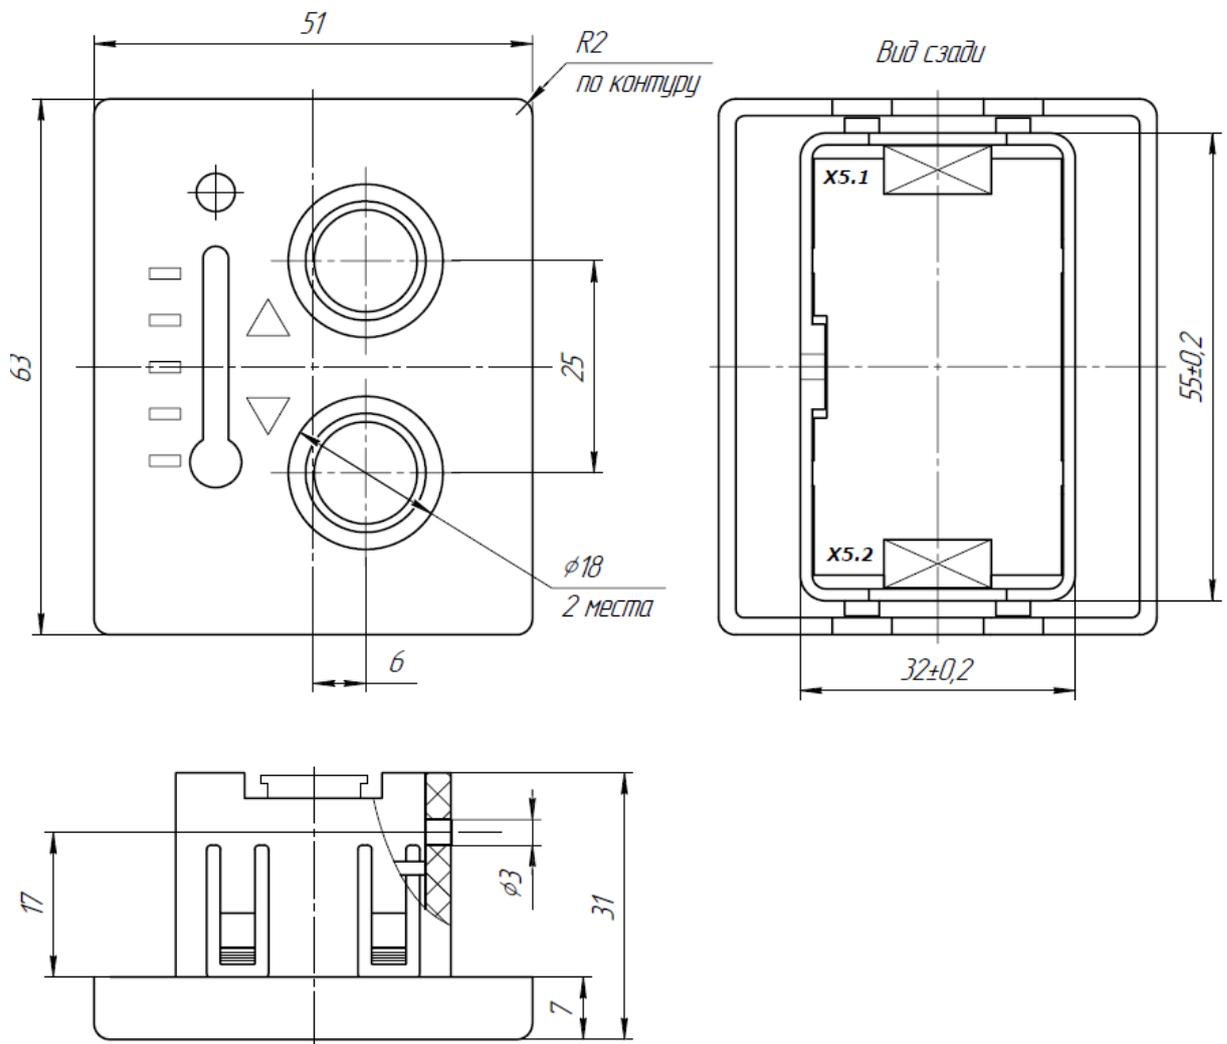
Внешний вид, габаритные и присоединительные размеры ПЭК-1.02
